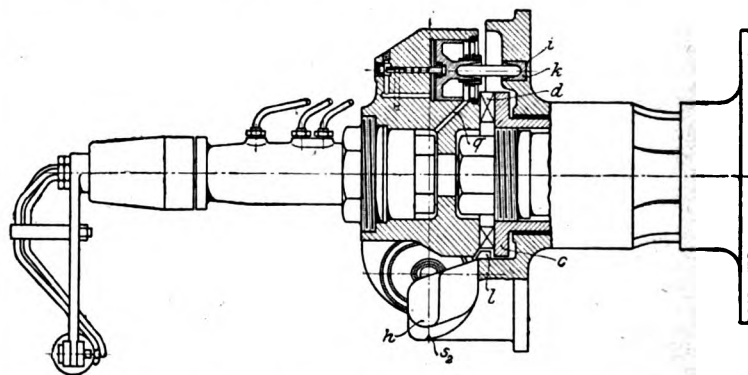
Seitenansicht der Meßnabe mit Schnitt durch gesteuerte Schubmeßdose.
